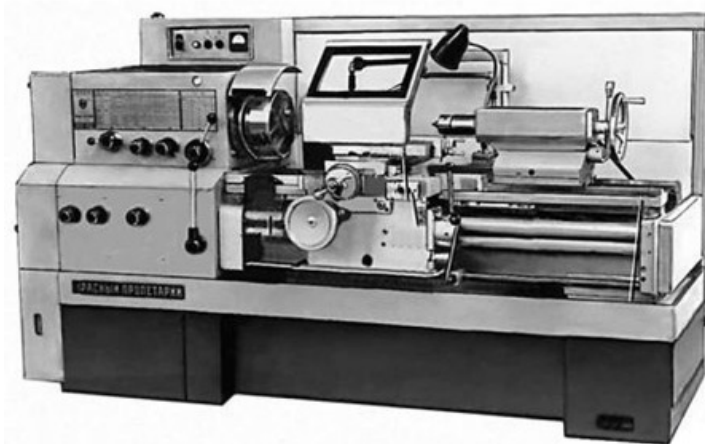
Общий вид токарно-винторезного станка 16К20
